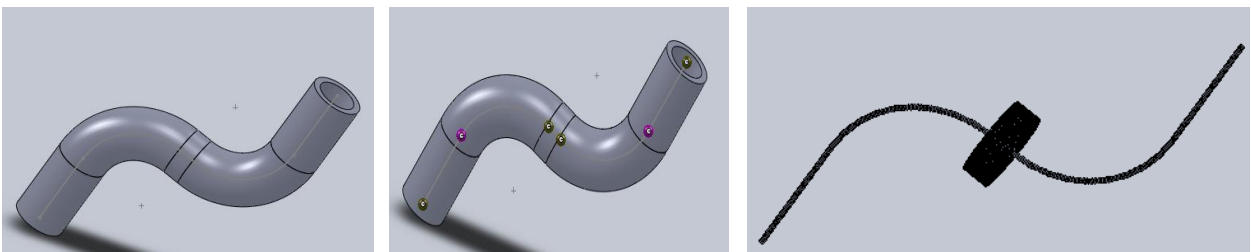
Modelado de un miembro estructural (a: miembro estructural, b: juntas, c: viga)
